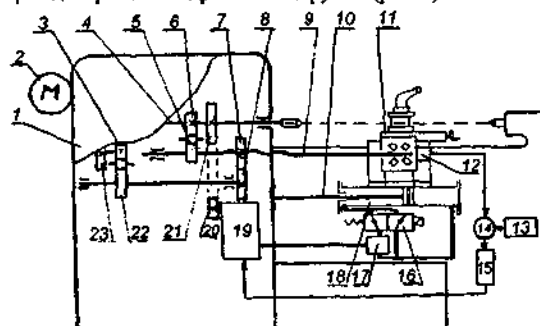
Схема привода токарного станка, с адаптивным управлением подачей
